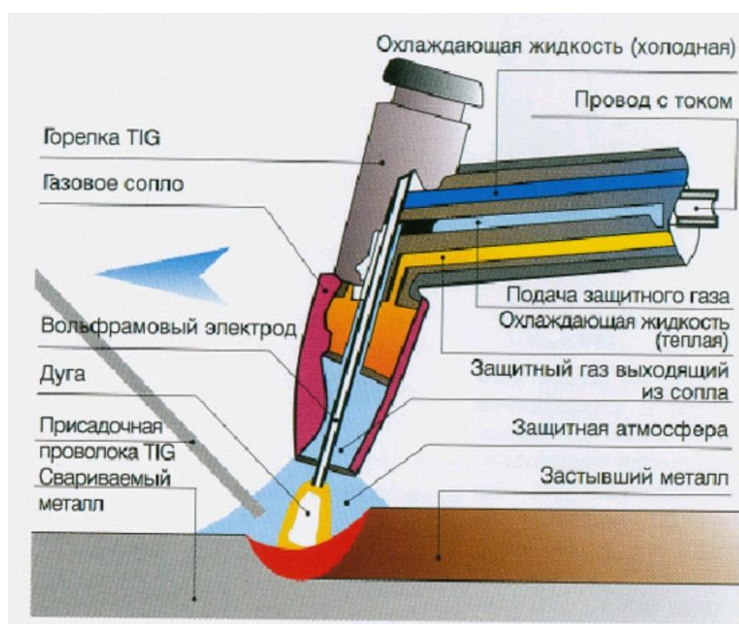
Схема сварки неплавящимся электродом в инертном газе
